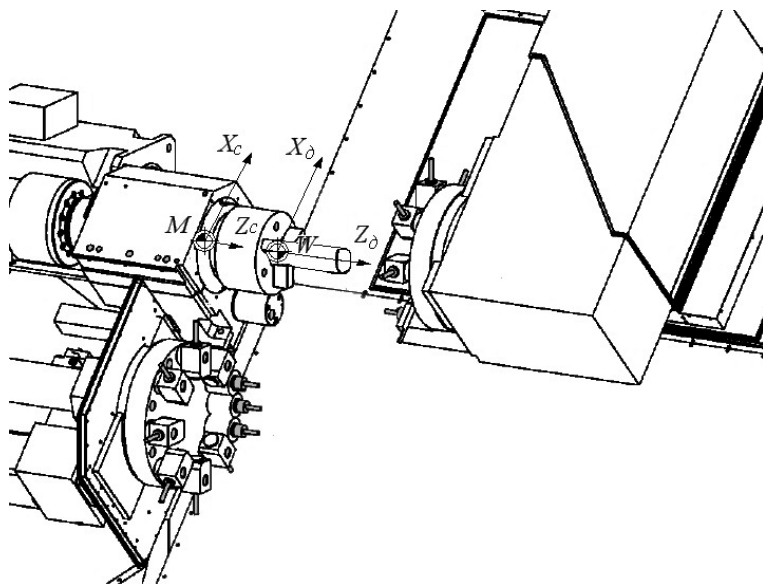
Положение нулевой точки детали W в системе координат токарного станка
